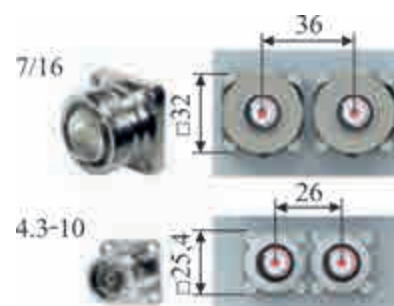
Внешний вид и размеры соединителей 7/16 и 4.3–10
